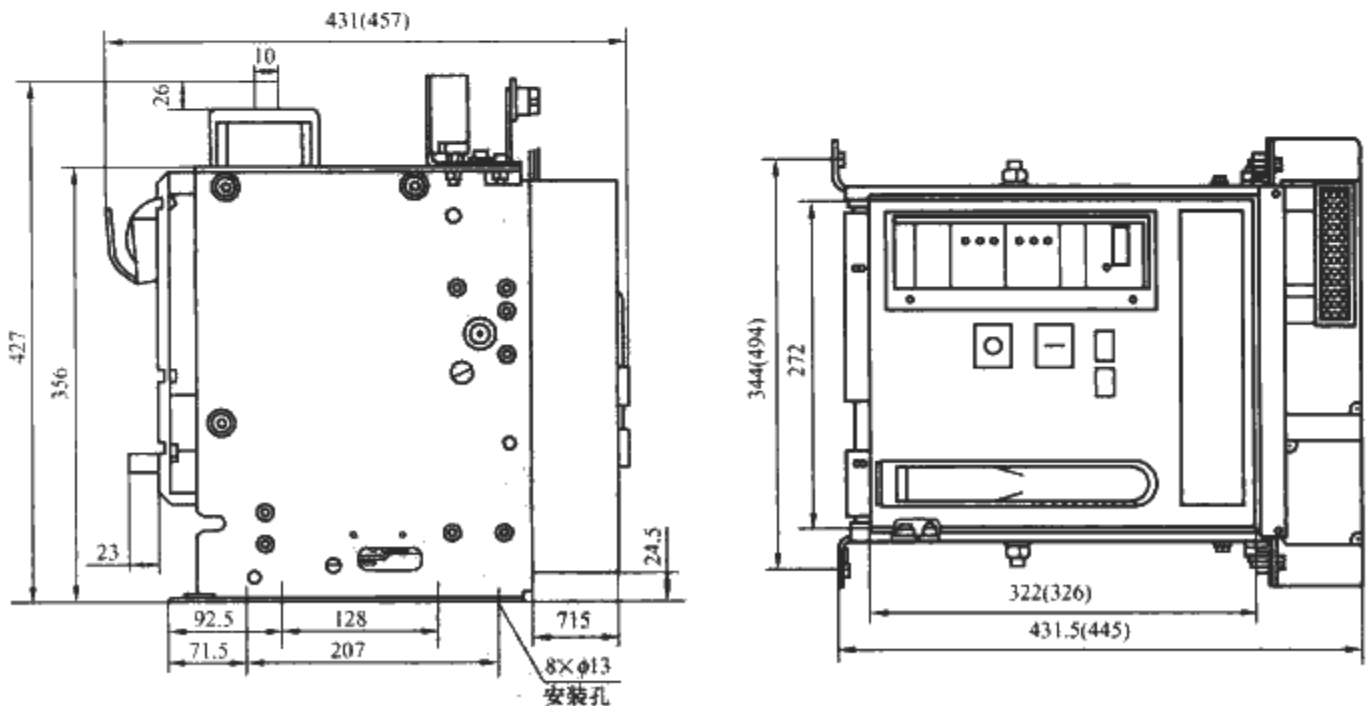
固定式真空断路器的外形尺寸和安装尺寸 (括弧中为 1600A 尺寸)
